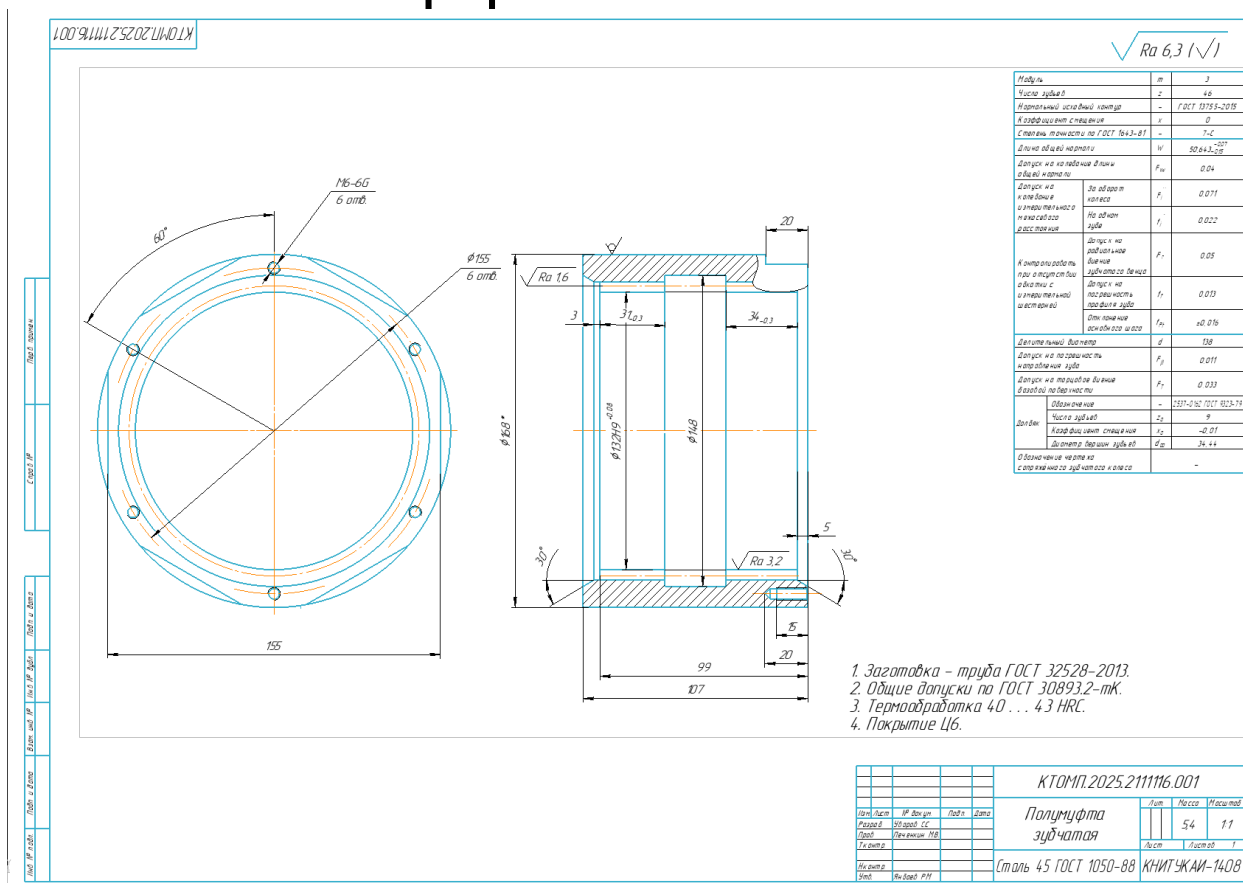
Рабочий чертёж детали «Полумуфта зубчатая»
